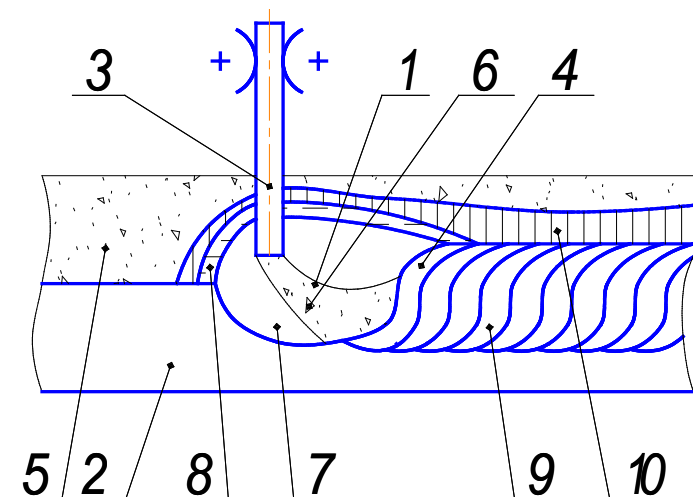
Автоматическая сварка под слоем флюса
